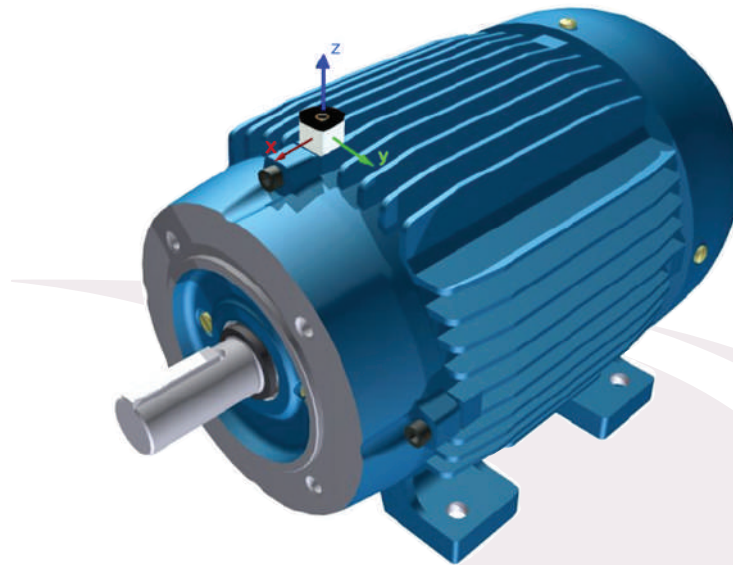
Posicionamento indicado do DynaLogger em um motor elétrico.
